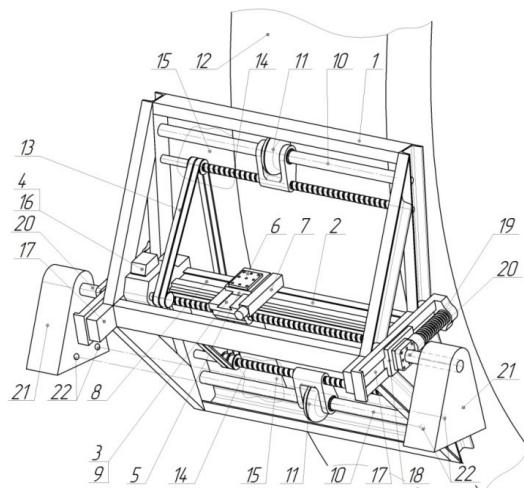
Схема станка для обработки поверхностей крупногабаритных деталей-тел вращения
